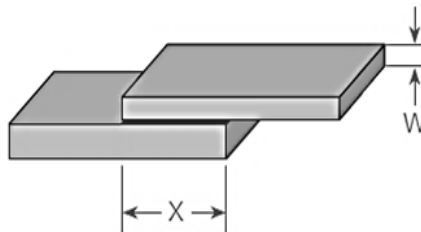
Diseño para calcular la longitud de la vuelta de la unión soldada [12].
